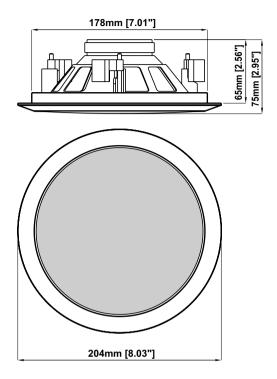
Dimensioni • Dimensions • Dimensions • Abmessungen • Dimensiones
